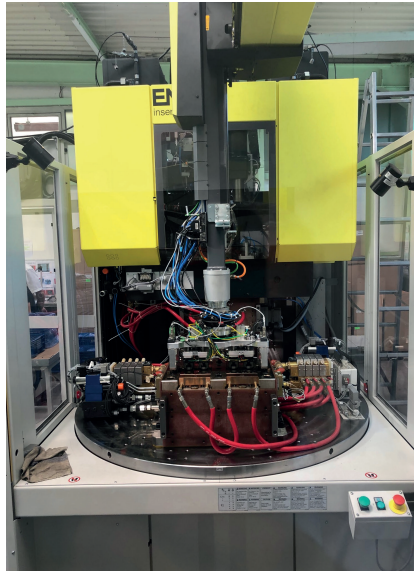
Vollautomatisierte Fertigungsanlage: Das 4-fach-Werkzeug für Stator- – bestehend aus einem Werkzeugober- und zwei auf dem Rundtisch montierten Werkzeugunterteilen – wurde inkl. Handling von Mühlbeyer konstruiert und gebaut © Mühlbeyer
